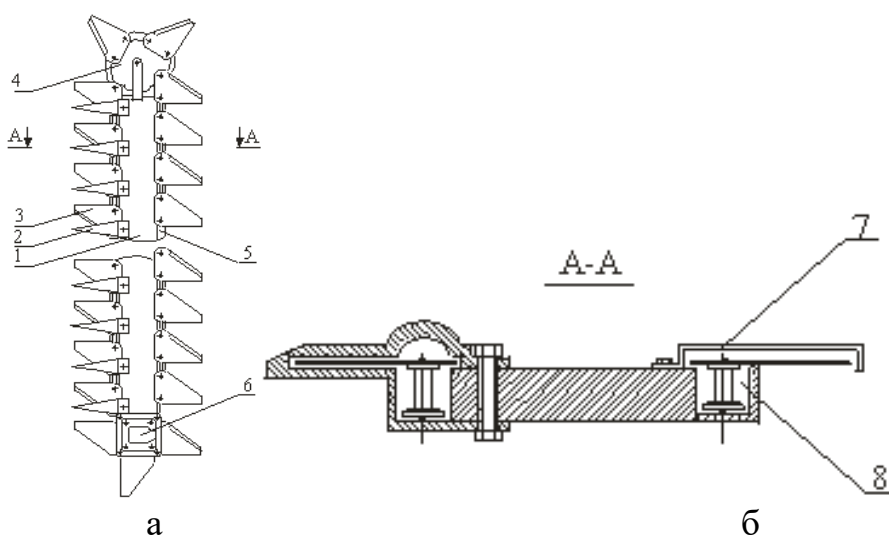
Схема цепного режущего аппарата (а-вид сверху, б-вид сбоку)
